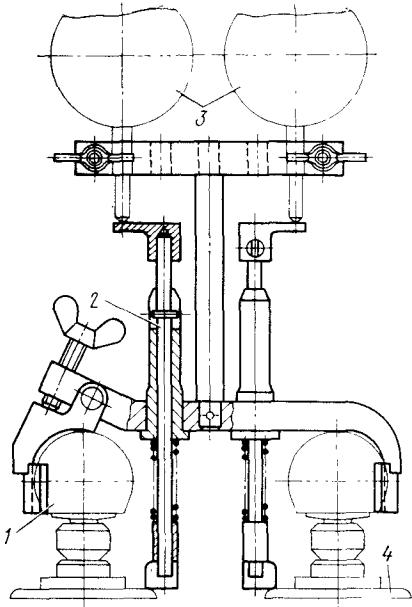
Приспособление для проверки зазоров на масло в гидротолкаталях и одновременности открытия клапанов:
